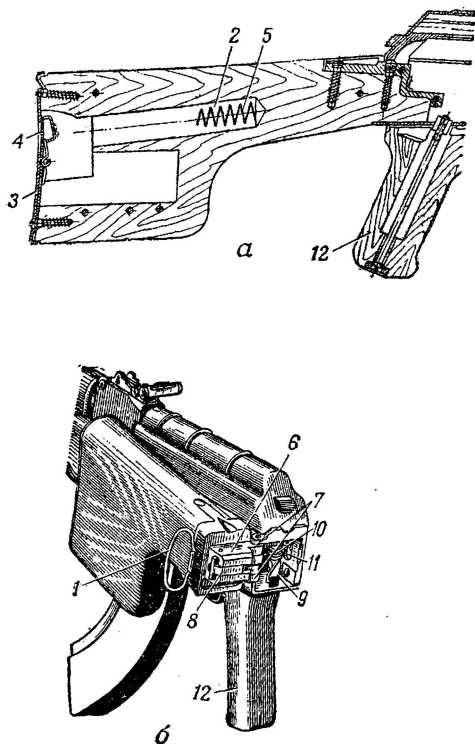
Приклад и пистолетная рукоятка пулемета:
